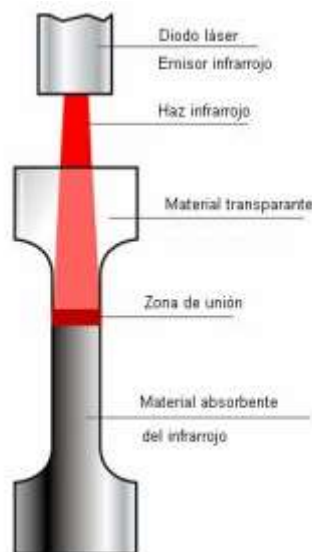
Esquema de soldadura por láser (Tecnología de los Plásticos, 2013)
